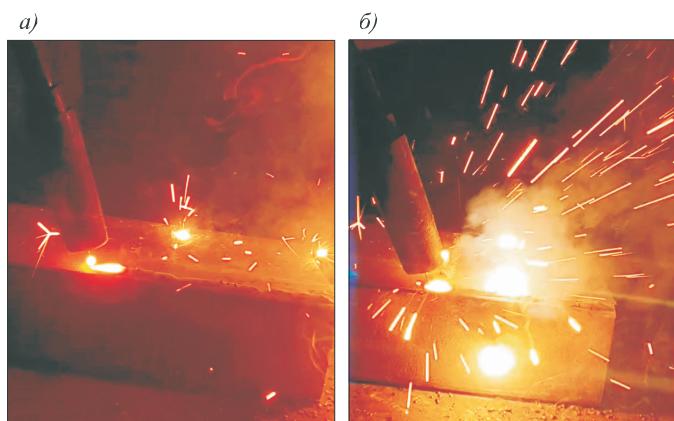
Разбрызгивание электродного металла при сварке оцинкованного профиля
